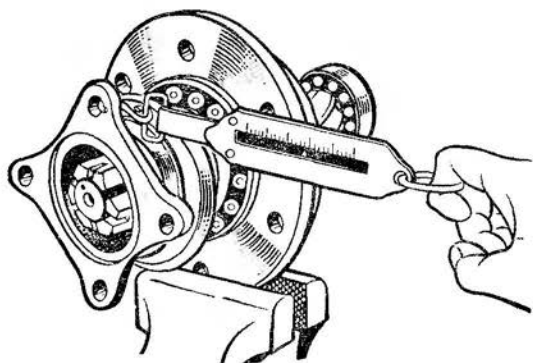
Проверка затяжки подшипников вала ведущей шестерни
